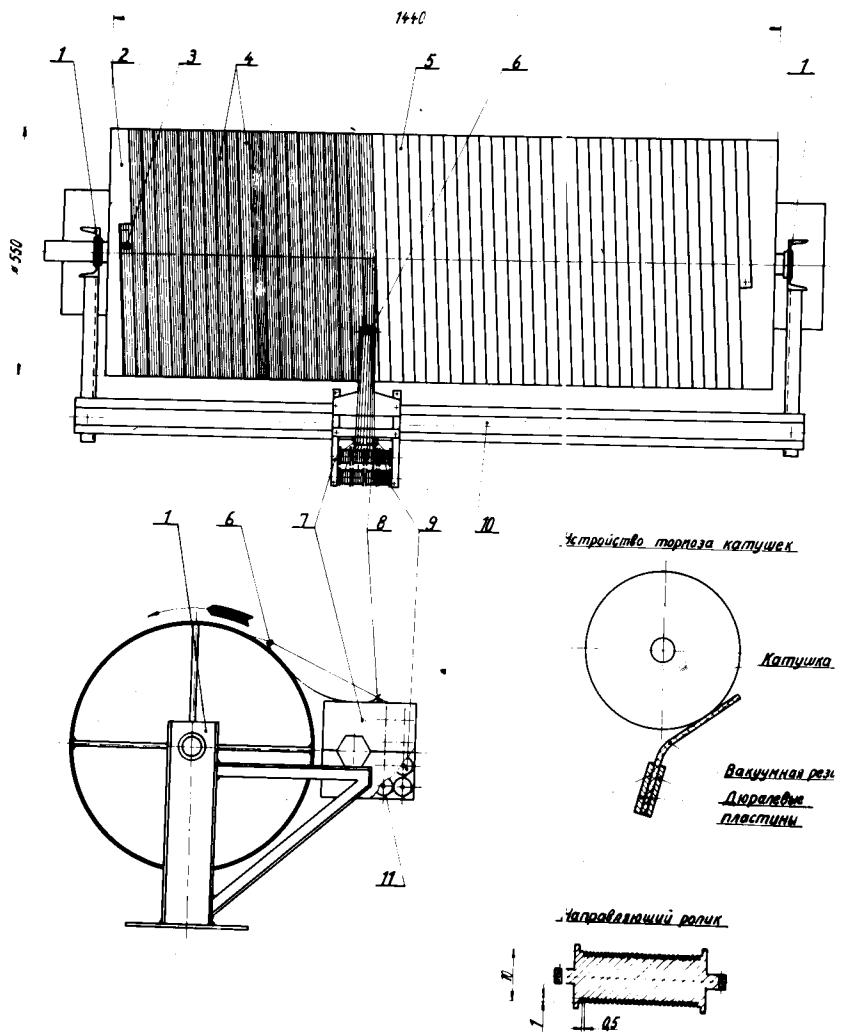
Устройство для намотки сверхпроводящей проволоки и медной подложки на цилиндрический барабан.
